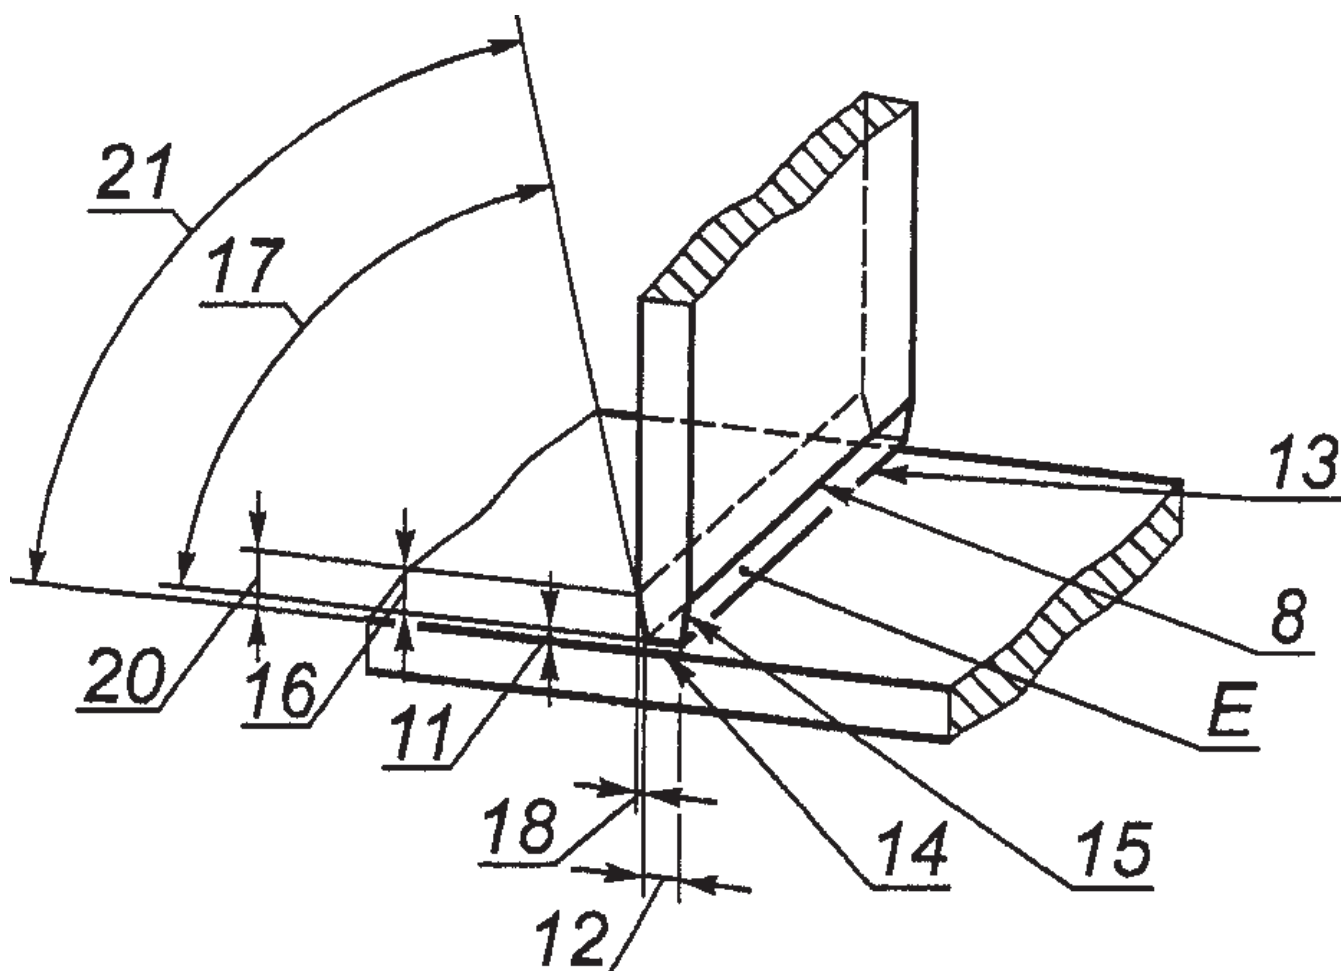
Подготовка под сварку таврового соединения с двусторонним скосом кромки Figure 7. Preparation for double-bevel T-butt welds Figure 7. pour soudures d'angle sur assemblage en T avec double chanfrein
